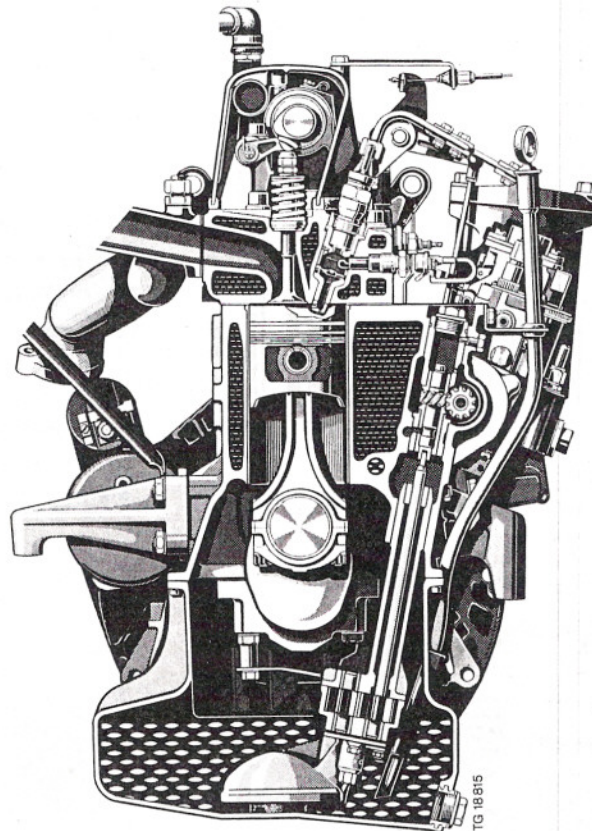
Motor Diesel 616 (Ejec. 616.936) – sección transversal
